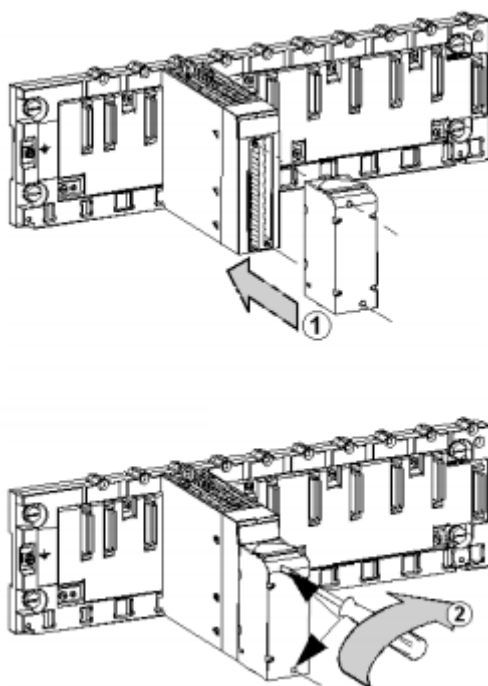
Instalación del Bloque del Terminal con 20 Pasadores / Installation du bornier 20 broches
